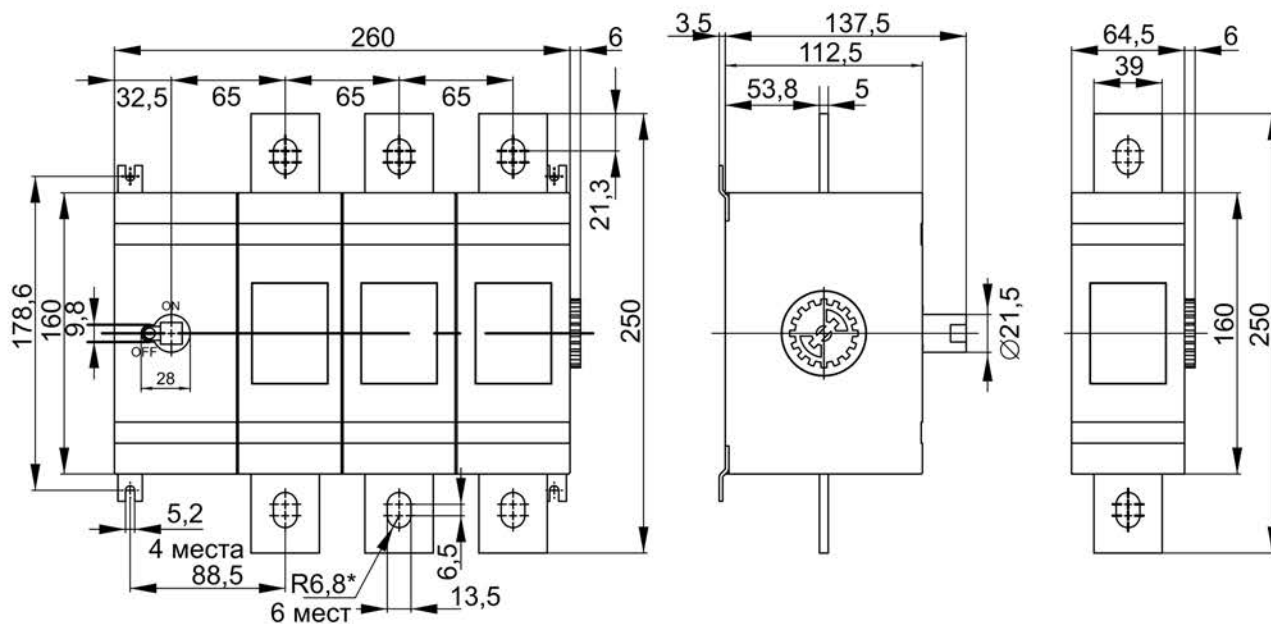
Габаритные, установочные и присоединительные размеры ВРК 630–800 А и дополнительного силового полюса 630–800 А / Figure 3 – Overall, mounting and connection dimensions of VRK 630–800 A and additional power pole 630–800 A
